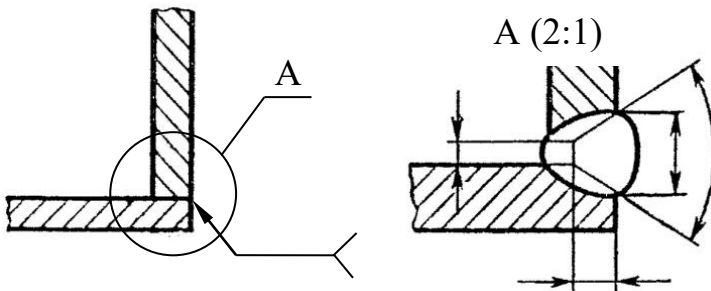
Виносний елемент (з'єднання зварюванням)
